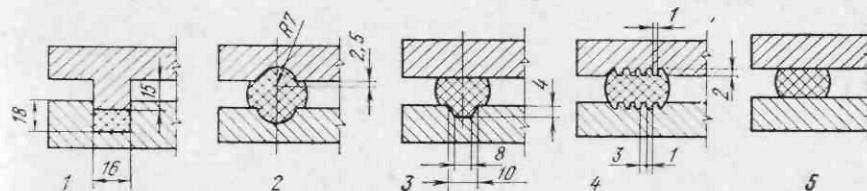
Конструкции уплотнений фланцевых соединений деталей
